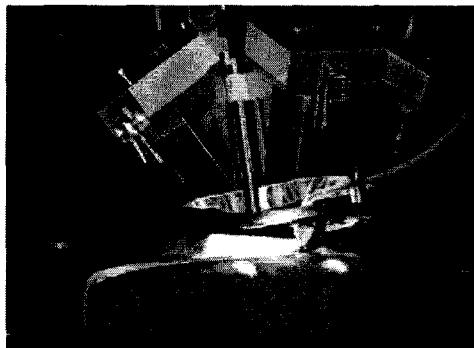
하이브리드 웰딩헤드 welding head
